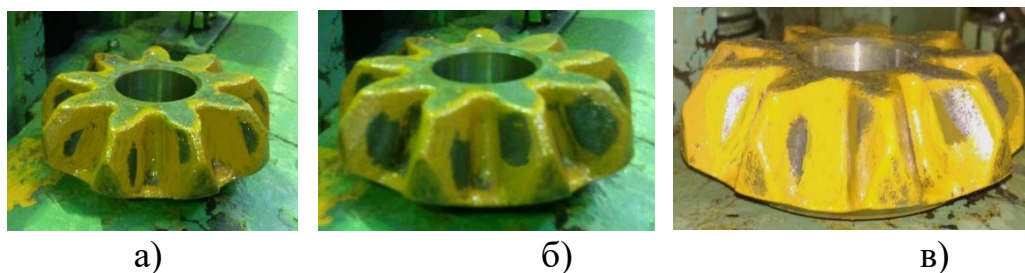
Опытные образцы после калибровочной операции без регулировки закрытой высоты штампа
